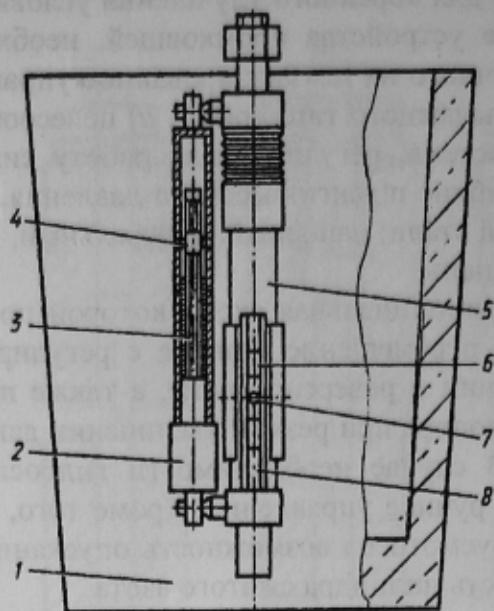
Схема стопорного механизма с электромеханическим приводом: 1 — промежуточный ковш; 2 — реверсивный электродвигатель постоянного тока; 3 — винт; 4 — гайка; 5 — корпус стопорного механизма; 6 — зубчатый сектор; 7 — рычаг; 8 — зубчатая рейка
